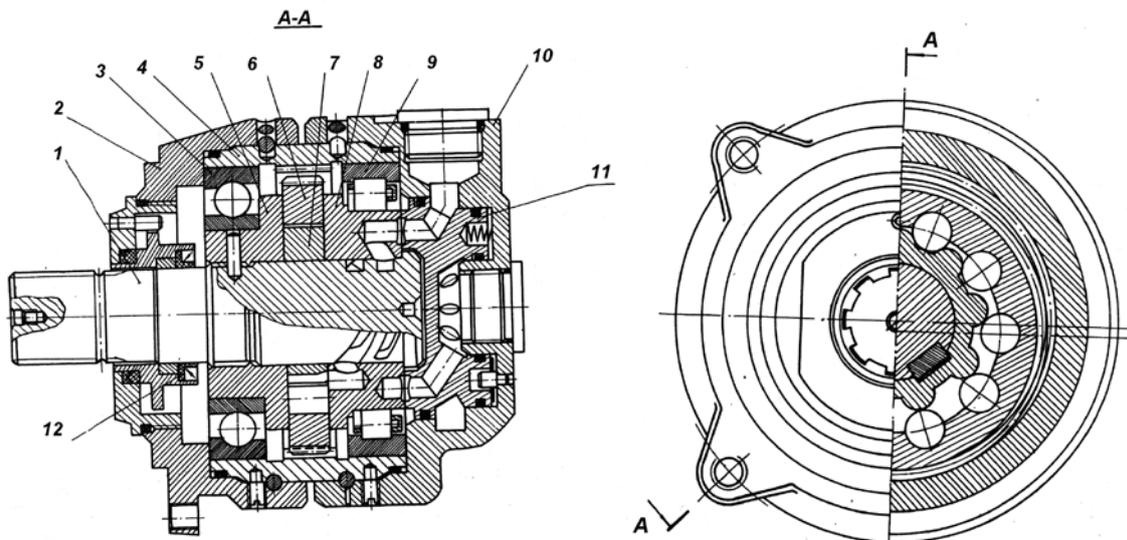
Гидромотор планетарно-роторный ГПР-Ф:
